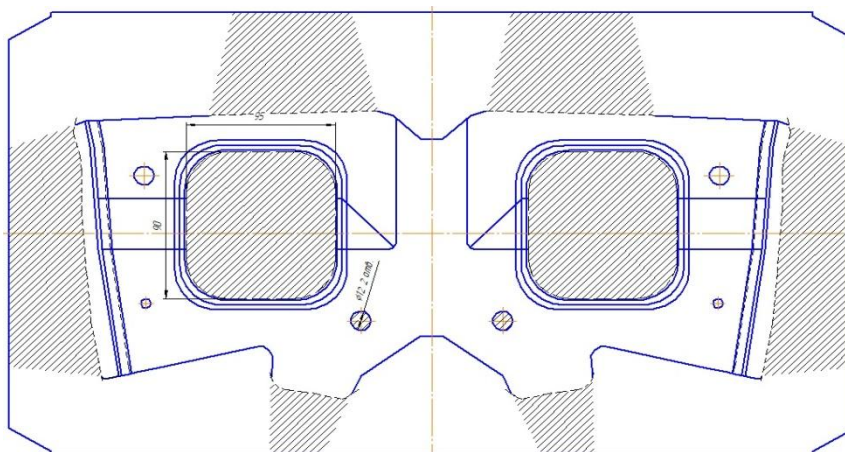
Обрезка 2-я, пробивка 3-я
